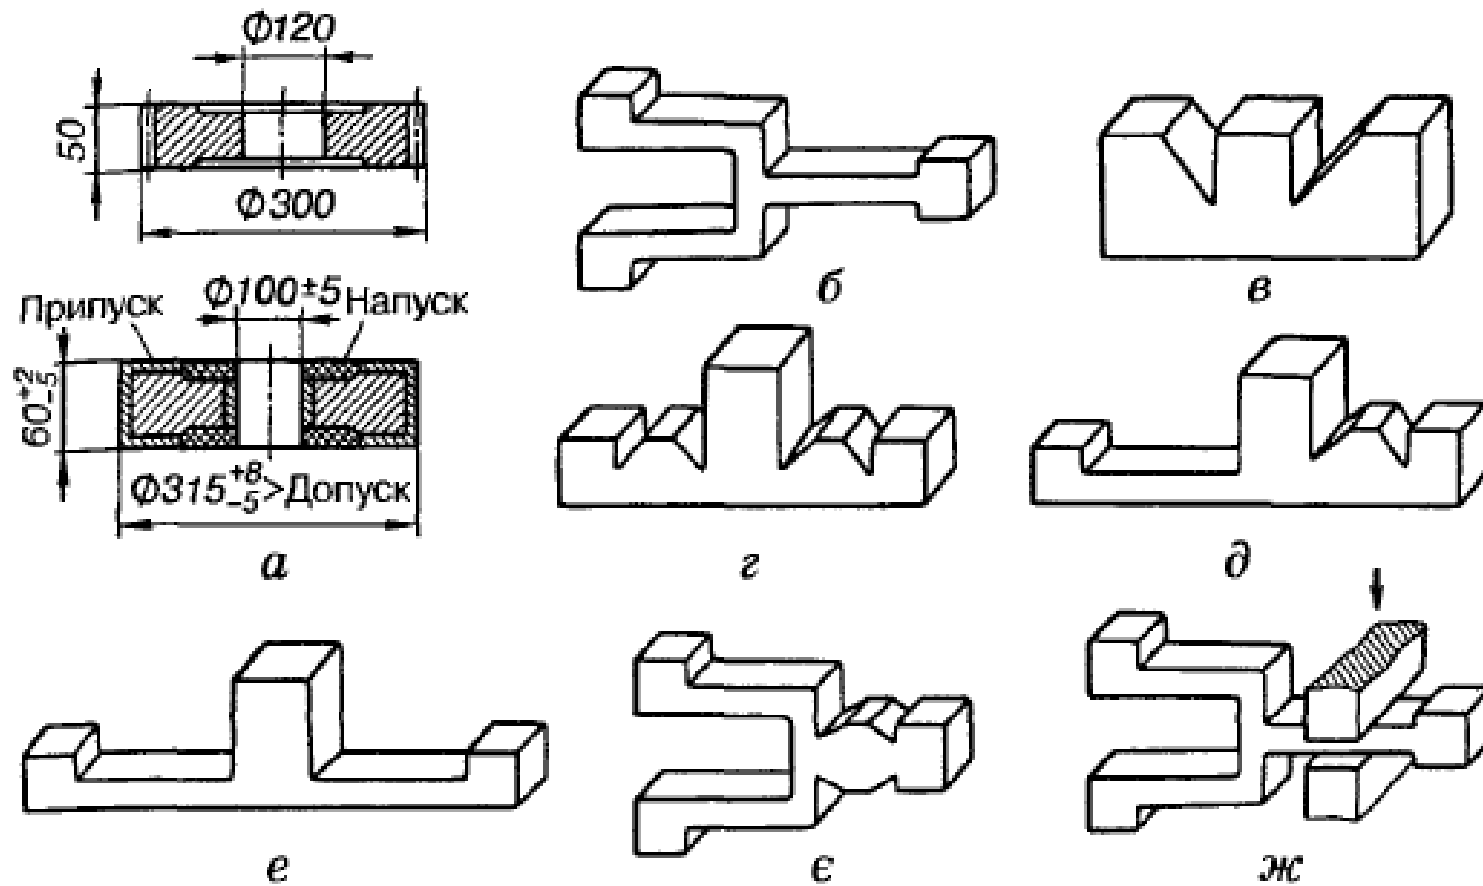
Креслення поковки шестерні і схеми технологічного процесу кування важеля з вилкою
